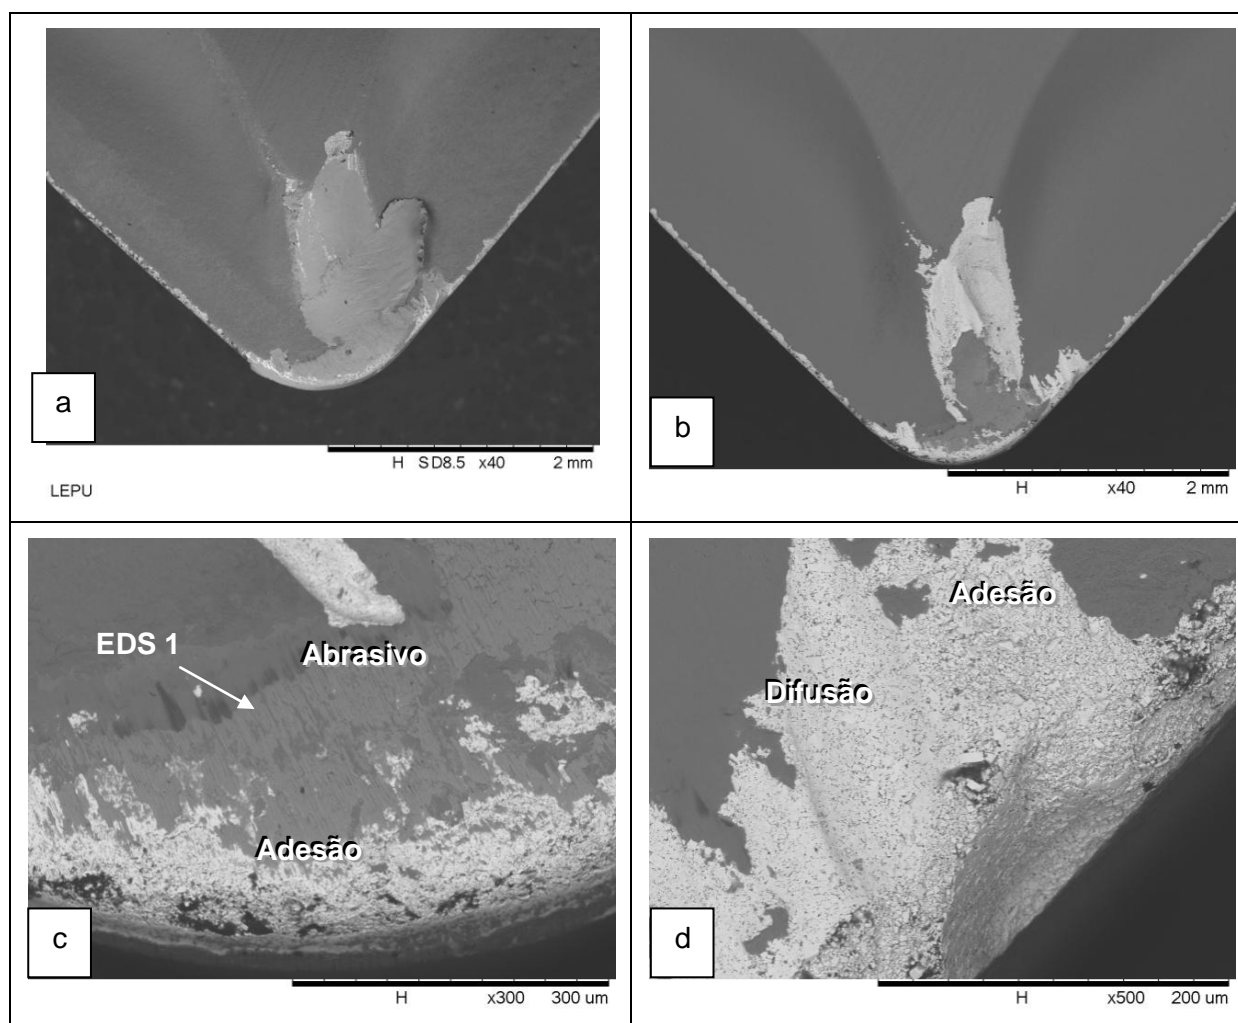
Detalhe dos mecanismos de desgaste presentes na superfície de saída da ferramenta utilizada para usinar o material B no ensaio de vida 1 ($v_c = 100,15$ m/min, $f = 0,35$ mm/volta e $a_p = 1,00$ mm). a) vista geral sem ataque químico; b) vista geral após ataque químico; c) detalhe da região do raio de ponta; d) detalhe do final da profundidade de corte
